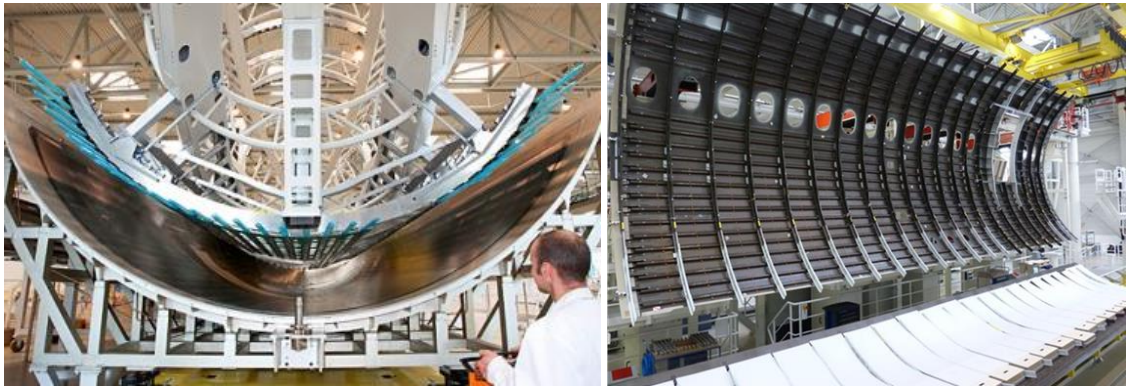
Paneles y ensamblaje de un fuselaje de aluminio.
